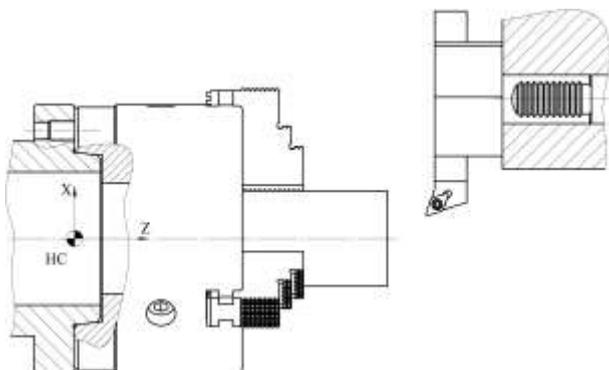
Общий вид рабочего пространства токарного станка с ЧПУ
